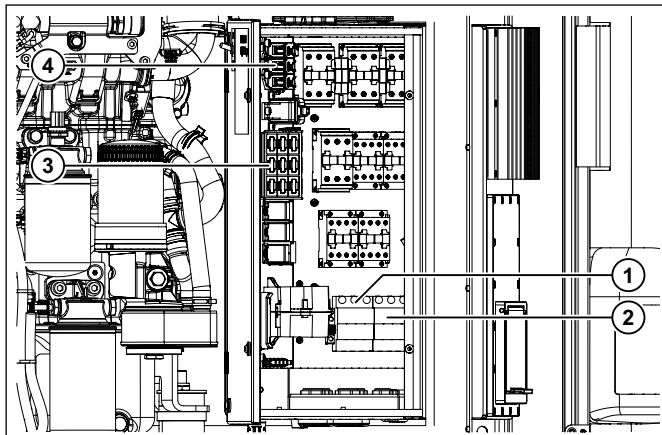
Vue d'ensemble des fusibles de la S.CU dc90
